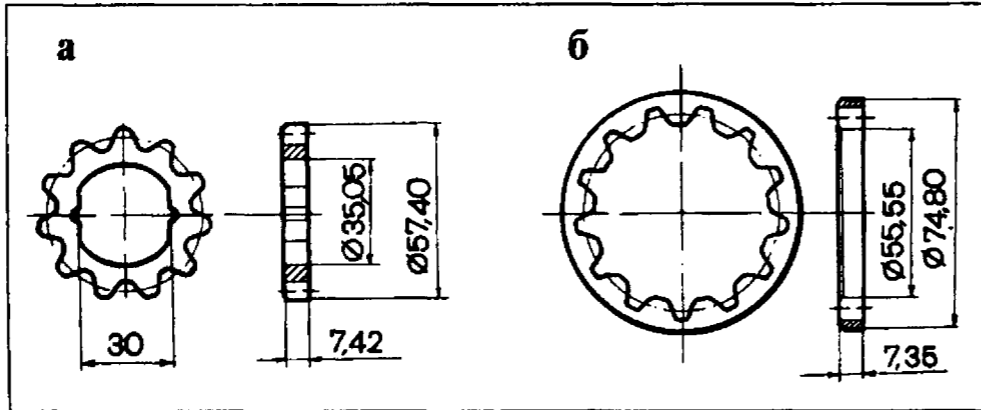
Предельные износы шестерен масляного насоса (размеры диаметров по вершинам зубьев даны для справок): а — ведущей шестерни; б — ведомой шестерни
